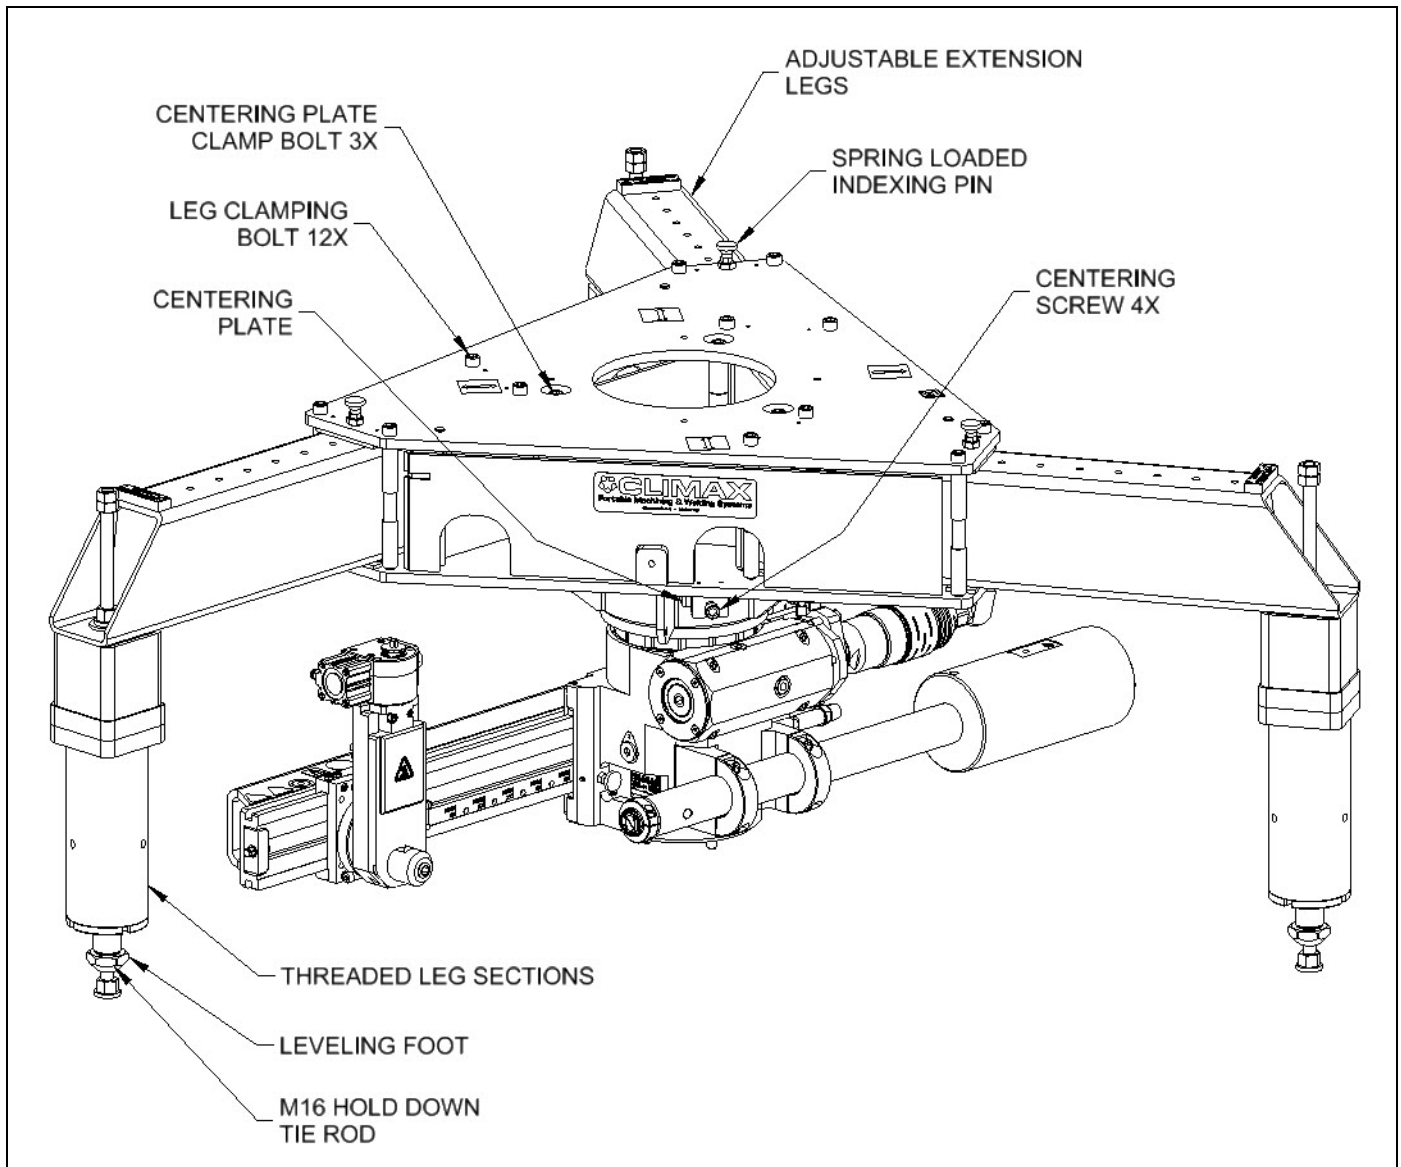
FF6300 ENSEMBLE DE MONTAGE DE
